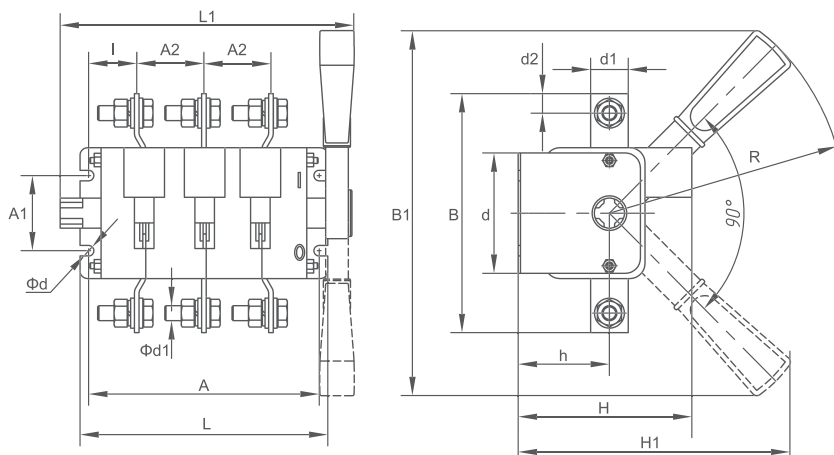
Выключатель-разъединитель универсальный трехполюсный на одно направление с д/г камерами, несъемная левая/правая рукоятка
